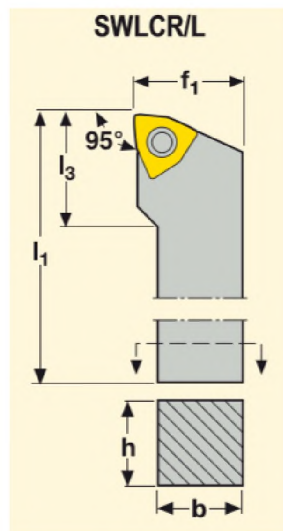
Державка SWLCR1616H06 [6, с.130]
